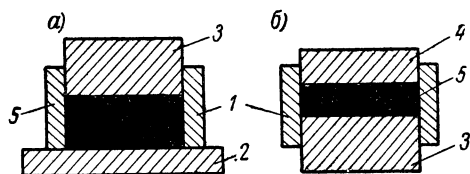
Схема съемной прессформы с подкладной пластиной для прессования заготовок высоковольтных конденсаторов: а — первое прессование; б — второе прессование.
